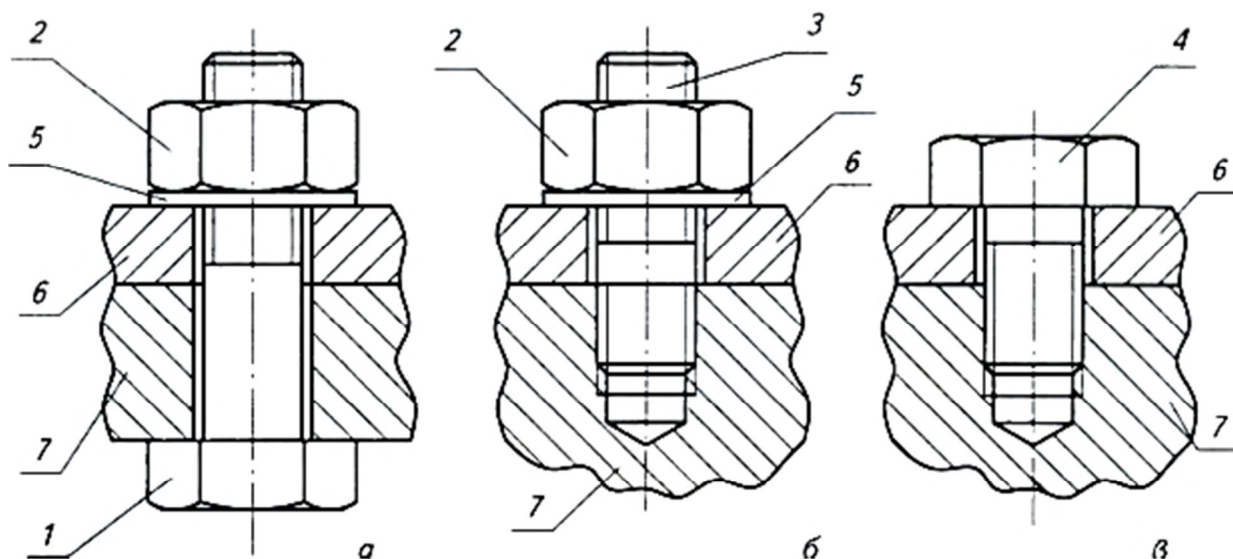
Резьбовые соединения: а — при помощи болта; б — при помощи шпильки; в — при помощи винта: 1 — болт; 2 — гайка; 3 — шпилька; 4 — винт; 5 — шайба; 6, 7 — соединяемые детали
